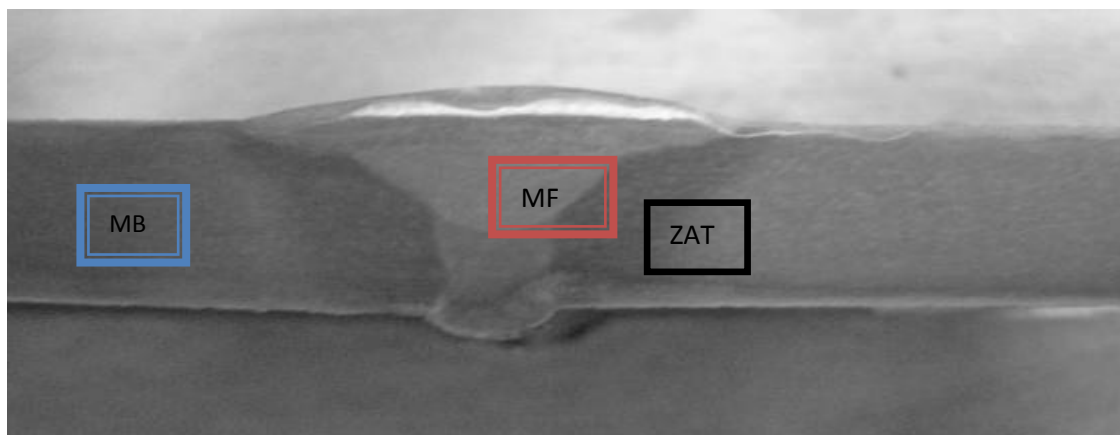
Film Radiographique de joint de soudure API X70
